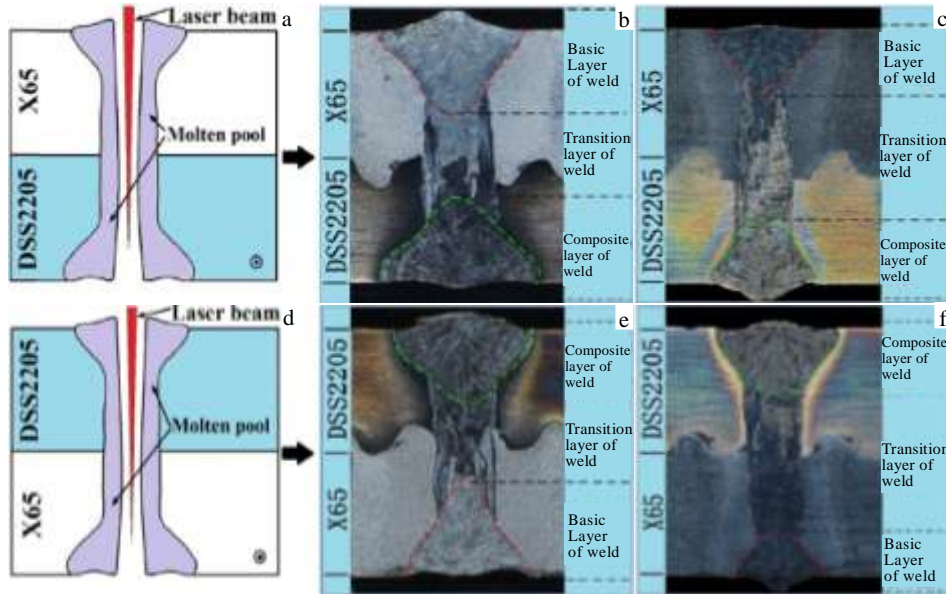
复合板激光焊接方式示意图及接头横截面宏观形貌
